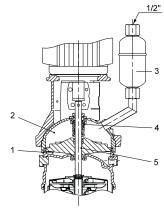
CR 10, 15, und 20 mit luftgekühlter Wellendichtungskammer
